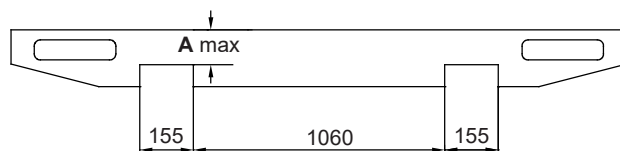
ZL-45-90, ZL-75-90, ZL-45-110, ZL-75-110
